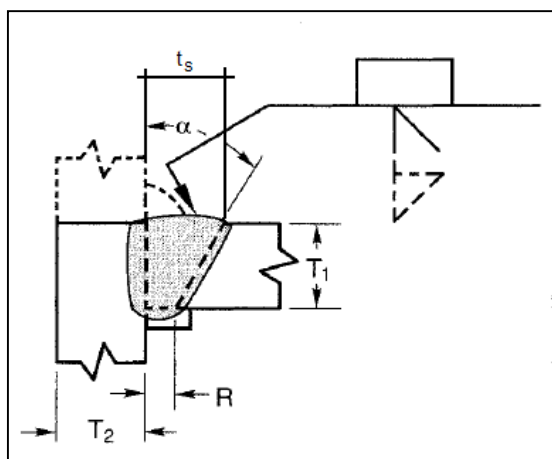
Geometría de soldadura de penetración completa
